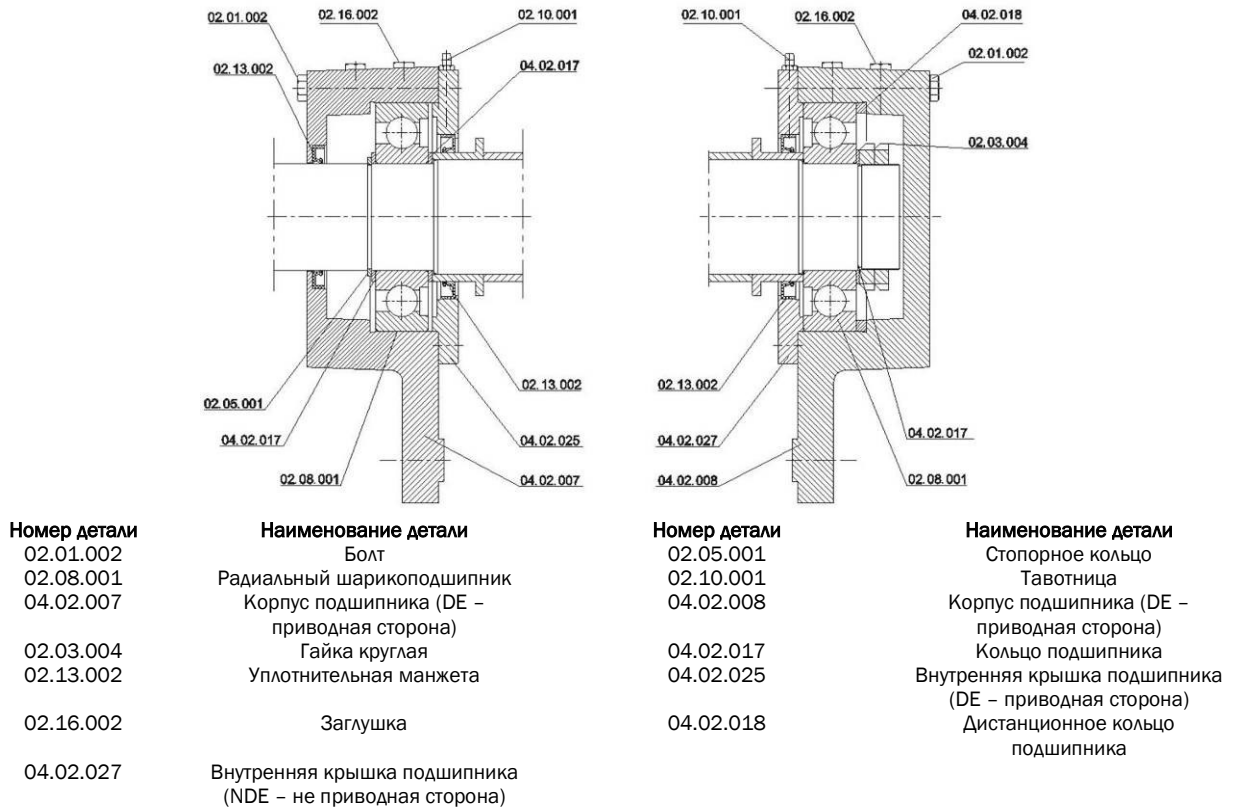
Подшипники в сборе тип С горизонтальным насосам типа С
